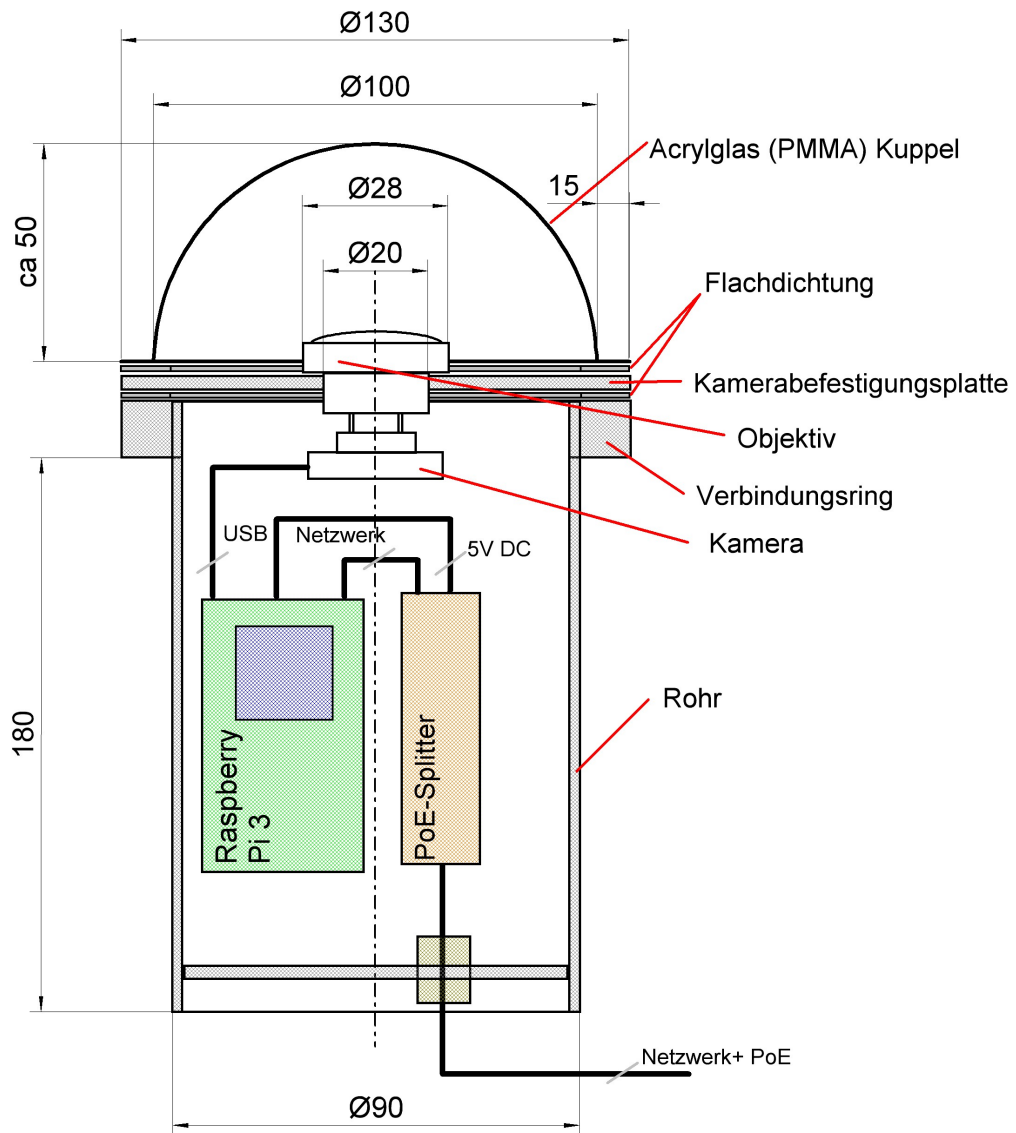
Technische Zeichnung des Gesamtgehäuses
